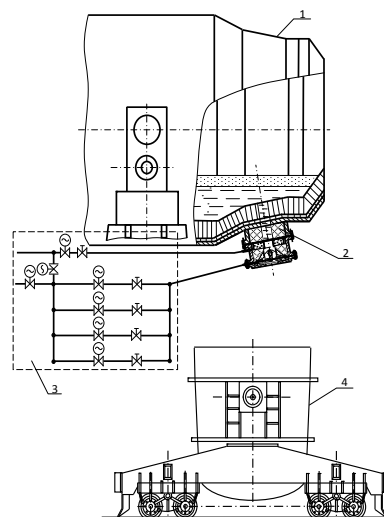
Общий вид системы газодинамической отсечки шлака. 1 – конвертер; 2 – устройство для отсечки; 3 – система подачи запирающего газа; 4 – сталеразливочный ковш.
